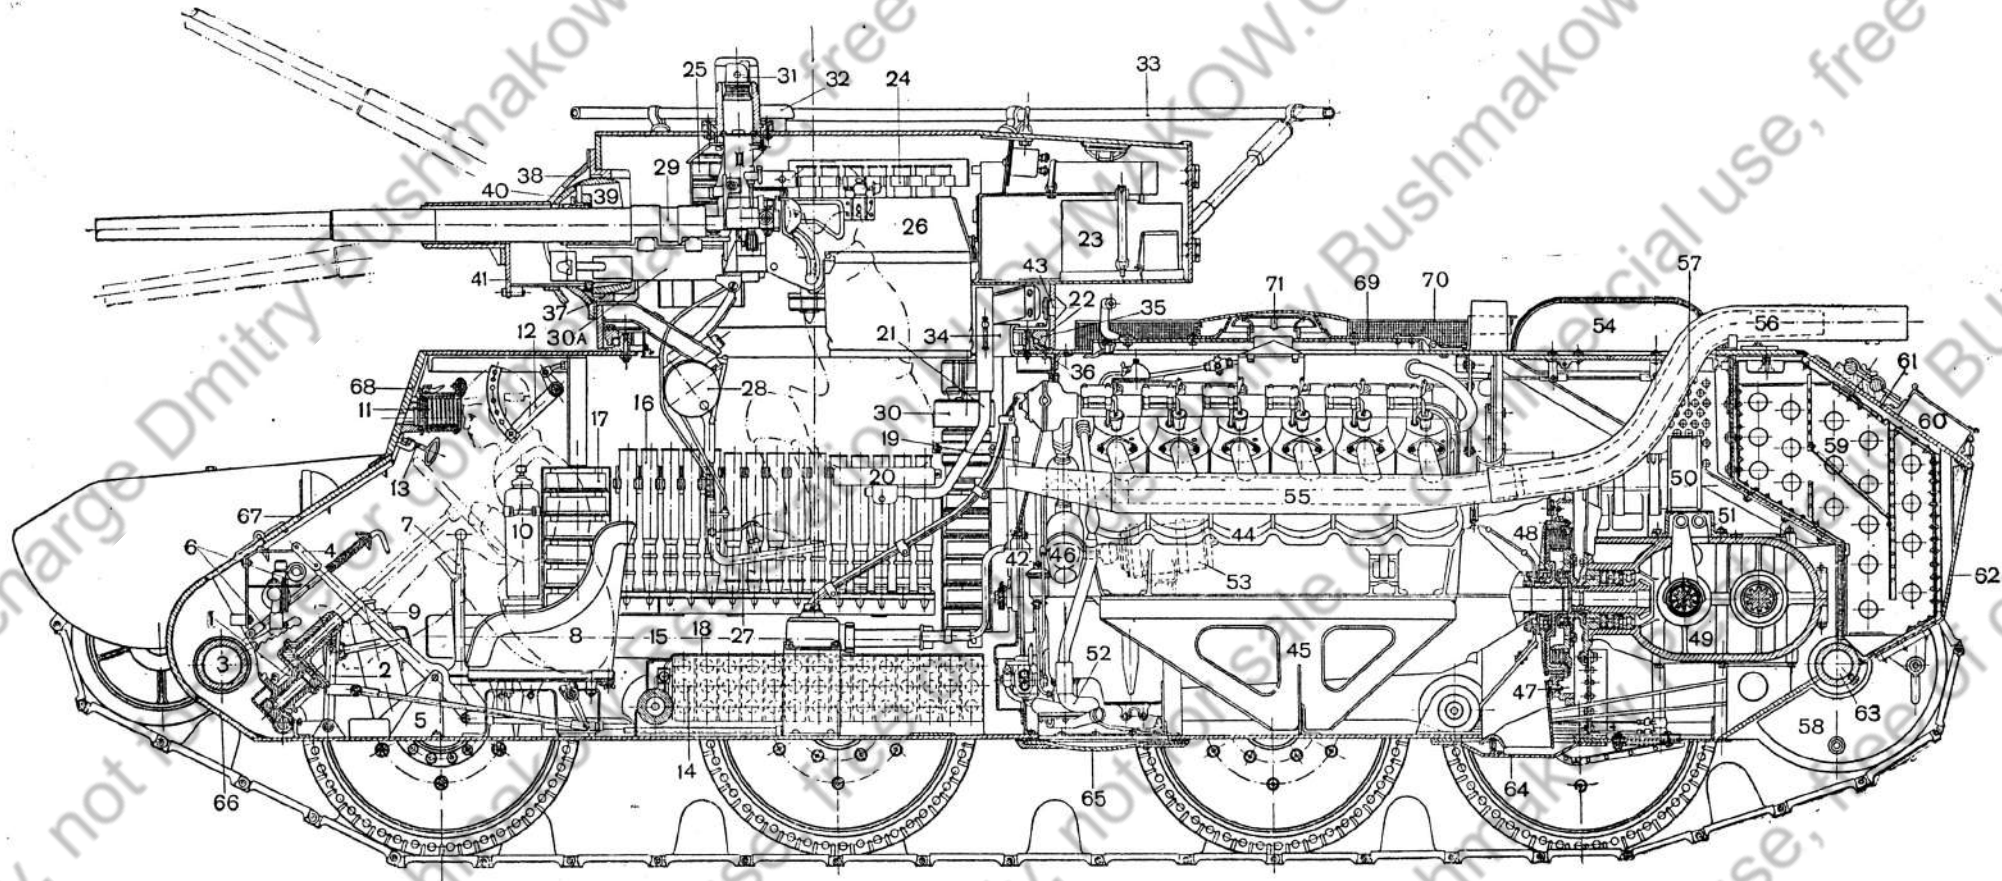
Общий вид танка БТ-7 (продольный разрез).
